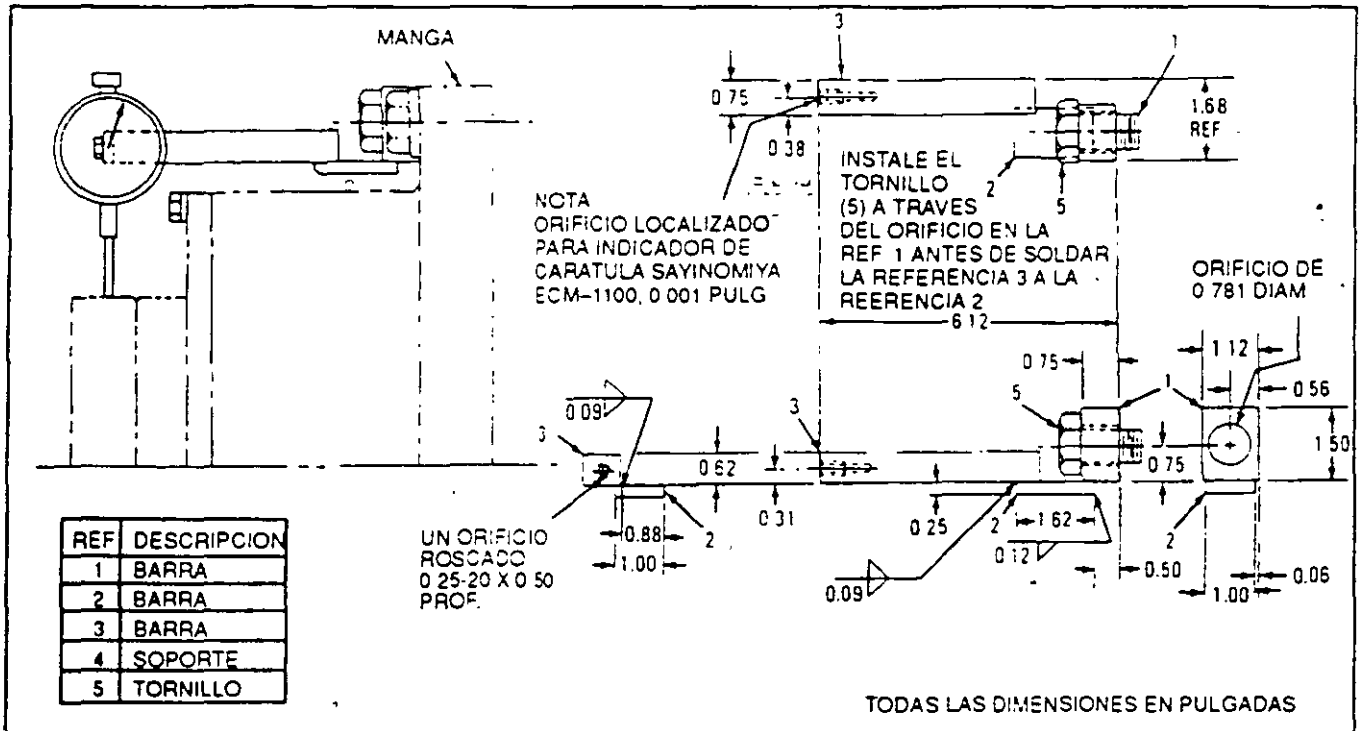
SOPORTE PARA EL INDICADOR DE CARATULA EN LA FLECHA IMPULSORA DEL COMPRESOR DEL LADO DEL MOTOR DIESEL. (SOPORTE: PARTE GE 41C624315G1. SOPORTE E INDICADOR: PARTE GE 41C624315G2). E-32866-S
